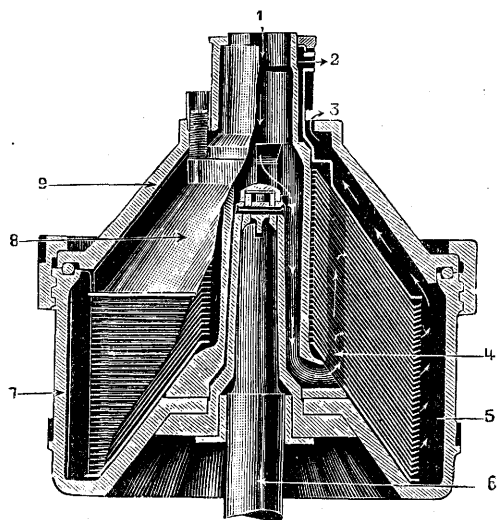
Ход сепарирования в цилиндре: 1—место поступления цельного молока; 2—выпускное отверстие для сливок; 3—то же для снятого молока; 4—тарелки; 5—место для скопления грязи; 6—ось цилиндра; 7—корпус цилиндра; 8—верхняя тарелка; 9—колпак цилиндра.
